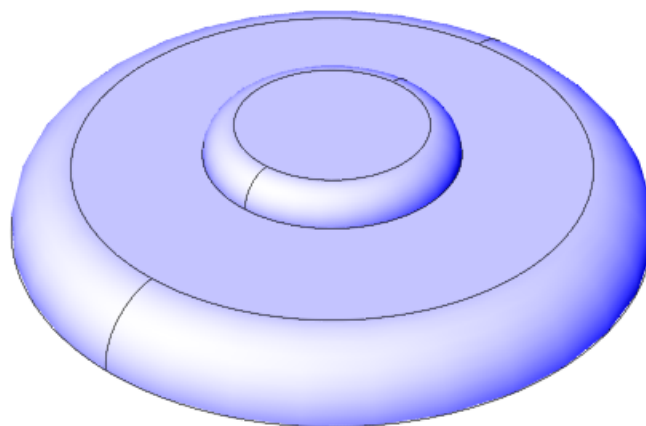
Beispiel für einen Flächenverband. Der Flächenverband besteht aus sechs Flächen. Vier Flächen sind nicht getrimmt. Eine Fläche ist getrimmt ohne Loch. Eine Fläche ist getrimmt mit Loch.
